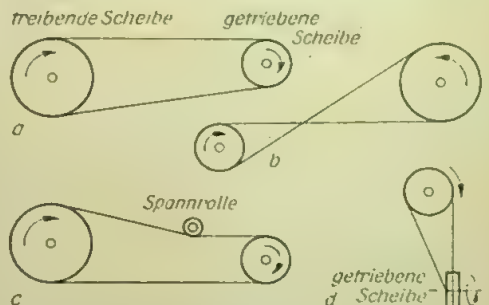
Riementriebe: a) offen, b) gekreuzt, c) mit Spannrolle, d) Winkeltrieb
